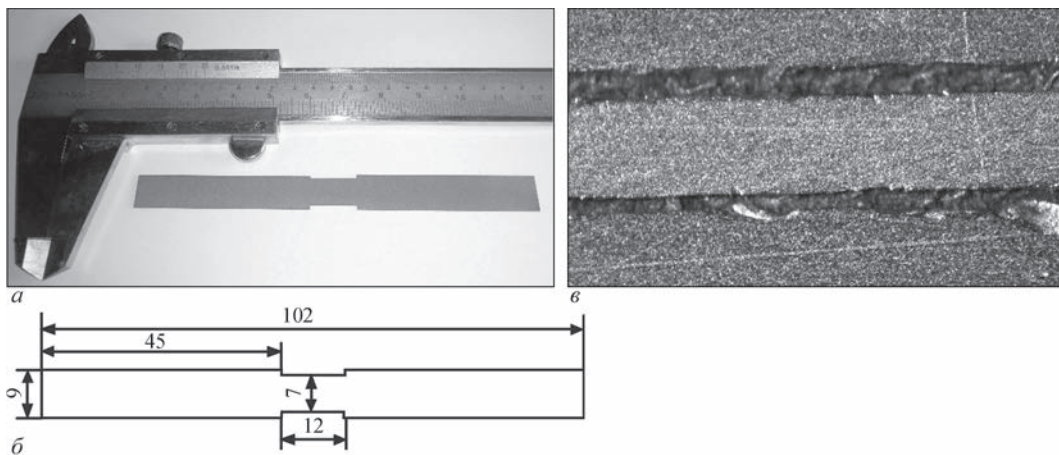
Нагрівач, виготовлений із монокристала вольфраму завтовшки 0,5 мм: а — загальний вигляд; б — креслення; в — шлиф поперечного перерізу
